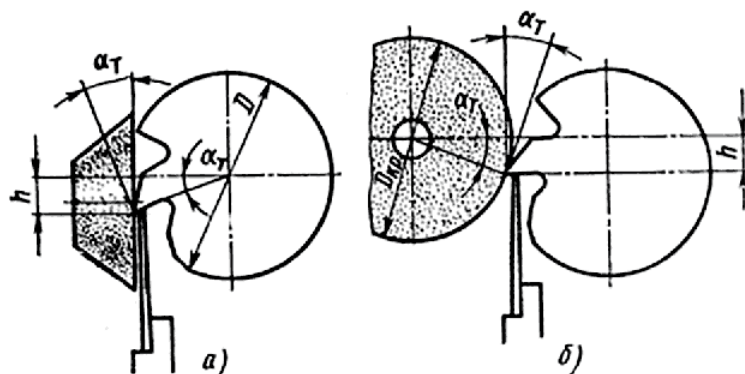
Установка шлифовального круга при заточке задней поверхности инструмента:
